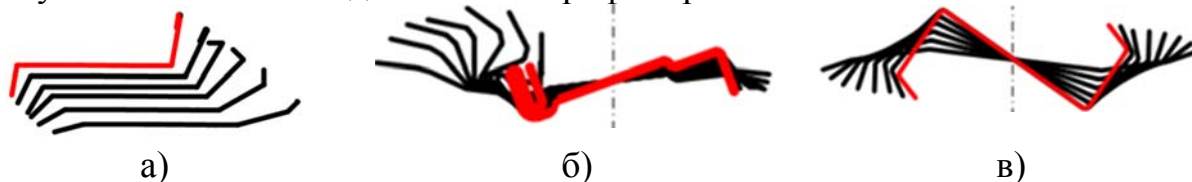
Схемы формообразования зетовых профилей в МИД:
